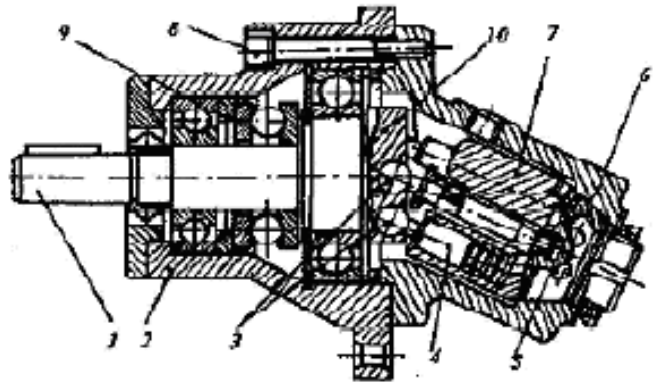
Pompă cu pistoane axiale cu corp înclinat
